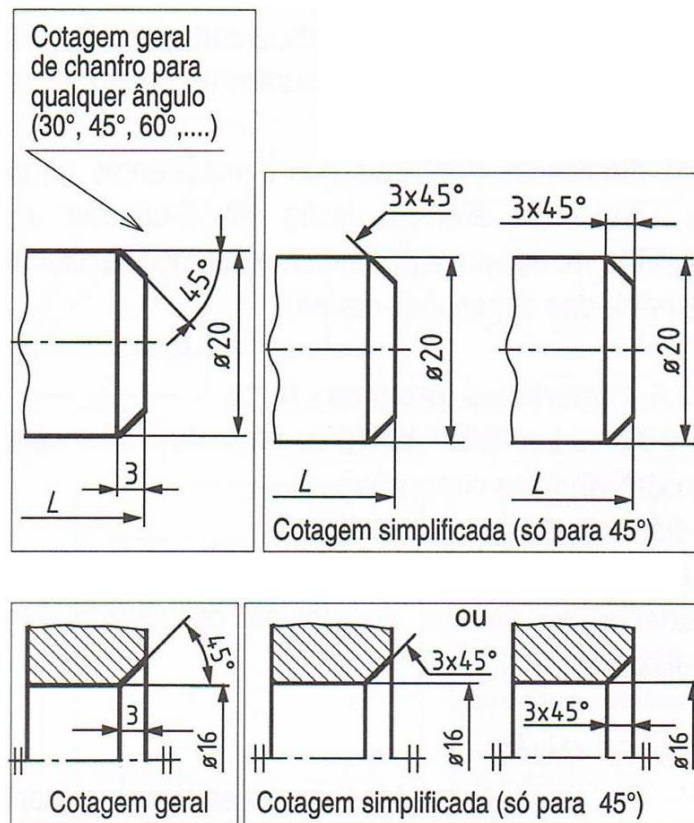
Representação em desenho técnico para cotação de chanfro.
